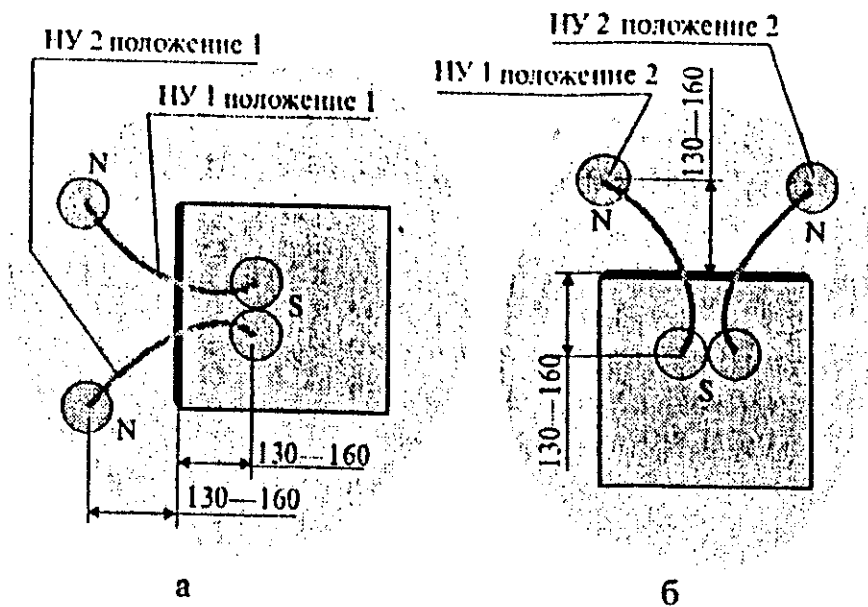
Контроль сварных швов накладки с размерами сторон (300—600) мм
